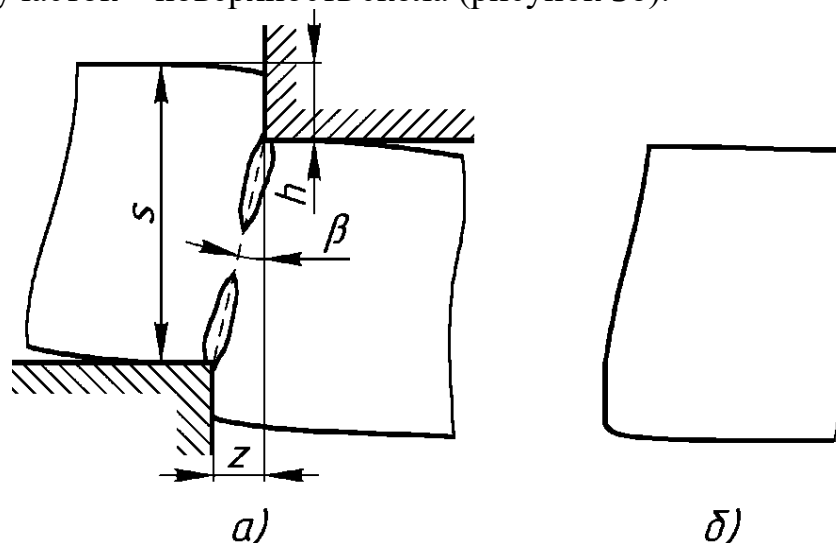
Образование трещин скола (а) и форма боковой поверхности отделенной заготовки (б)
